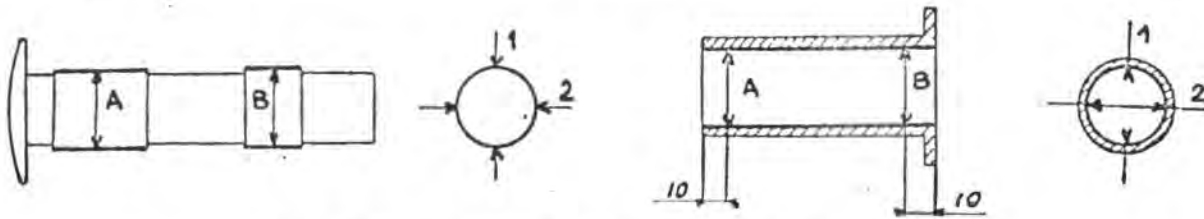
DIMENSIONS DES POUSSOIRS ET DE LEURS GUIDES
